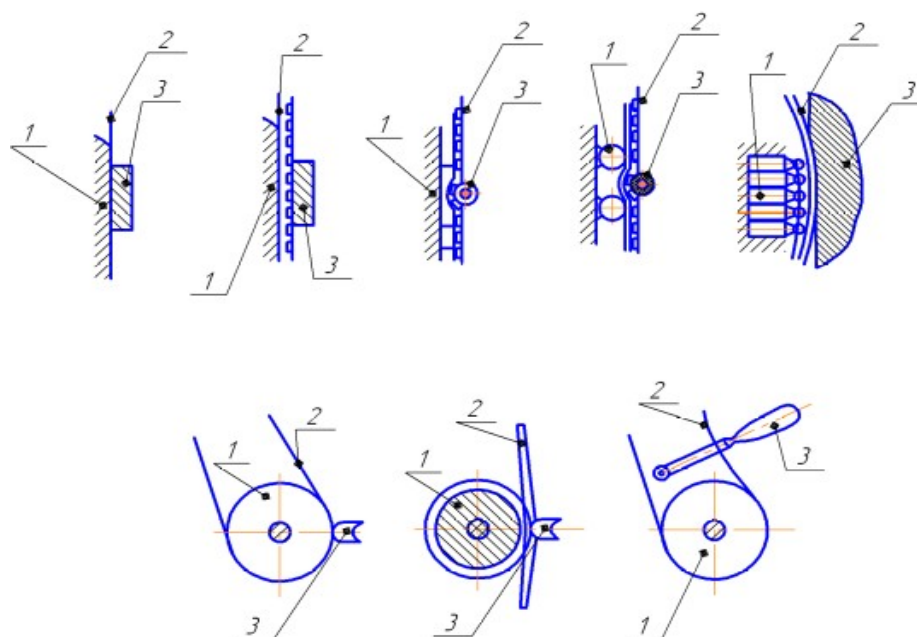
Схемы полирования абразивными лентами поверхностей заготовок: 1 – прижим; 2 – абразивная лента; 3 – обрабатываемая заготовка
